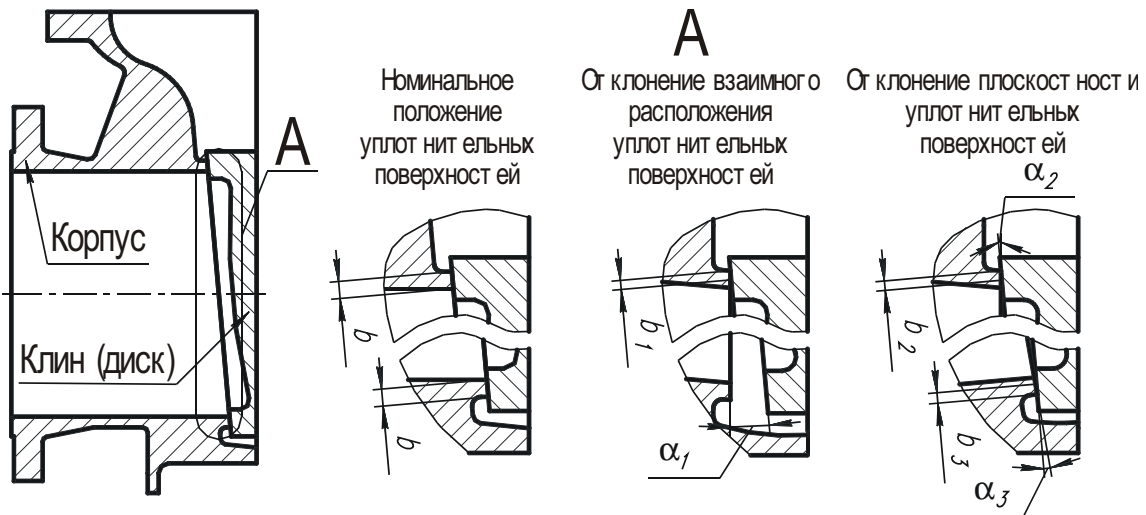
Уплотнительные поверхности клиновой задвижки и основные виды нарушений их взаимного расположения (показаны условно)
